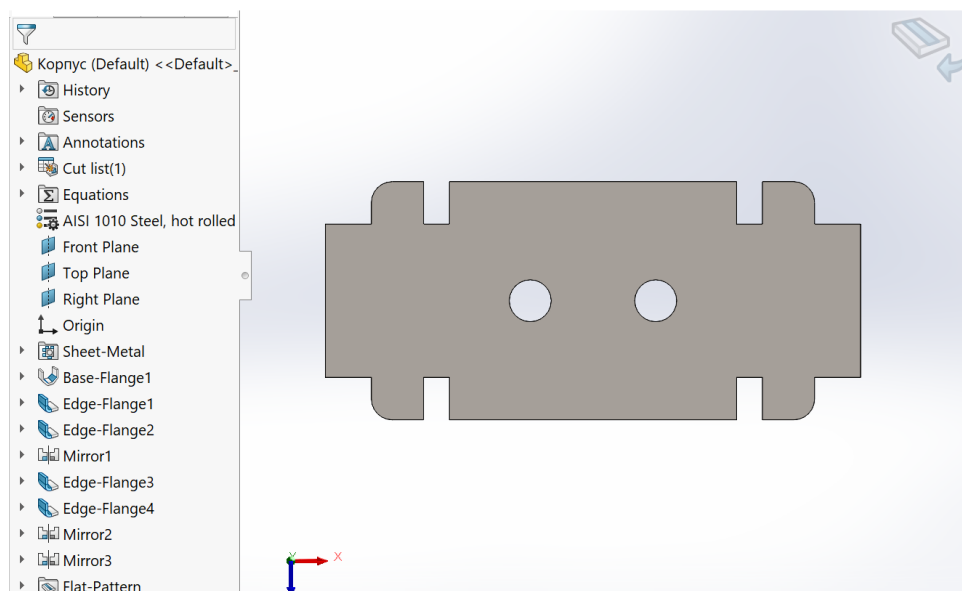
Розгортка тривимірної моделі деталі «Корпус»
